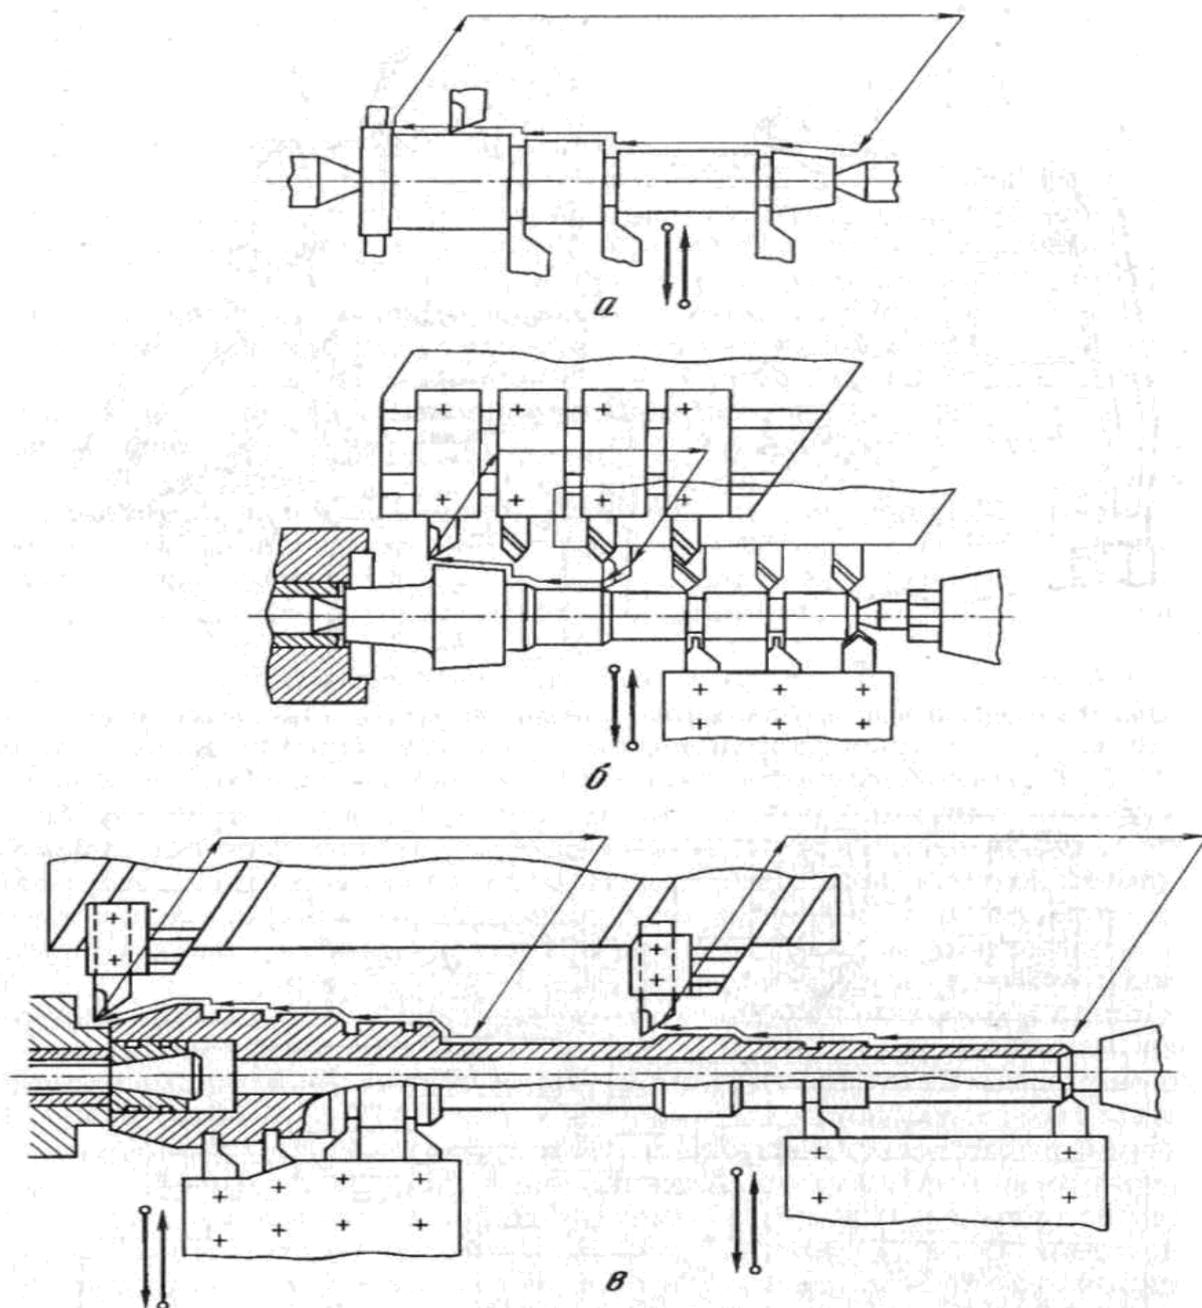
Схема обработки заготовок на многолезковых копировальных полуавтоматах: а - одним резцом, б – блоком резцов, в – с двух копировальных суппортов.
